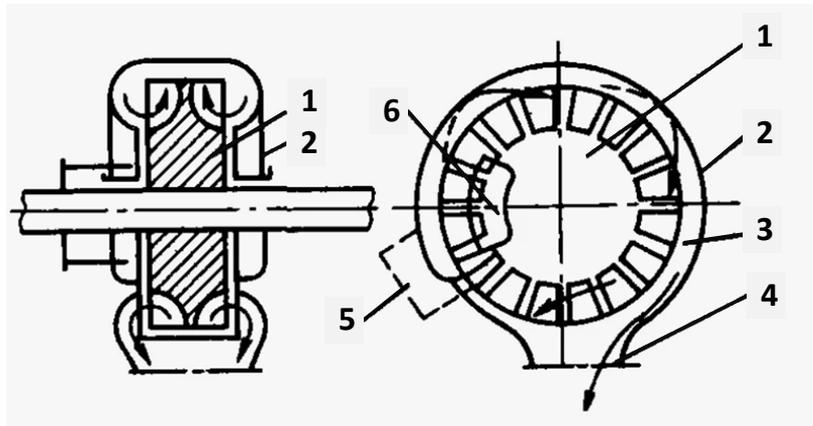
Вихревой насос: 1 – колесо; 2 – корпус; 3 – полость; 4 – напорный патрубок; 5 – всасывающий патрубок; 6 – уплотняющий выступ
